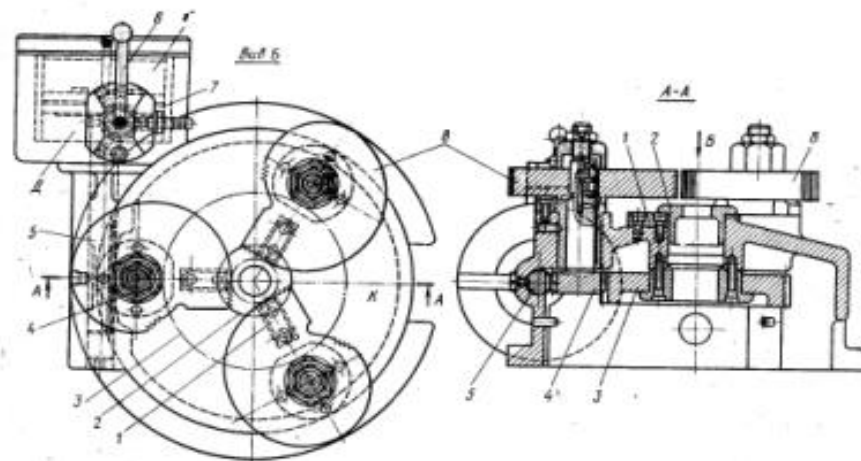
Універсальний трикулачковий самоцентруючий патрон з пневмоприводом
